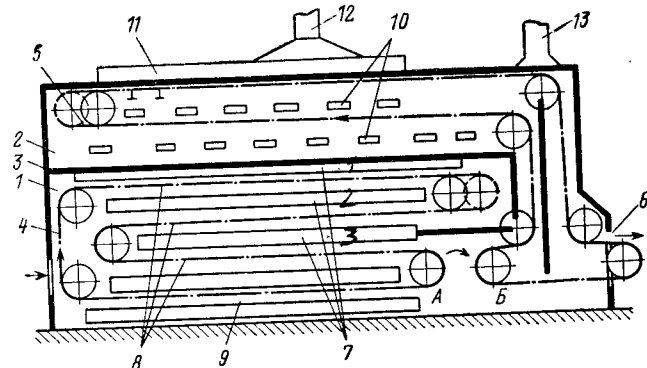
Схема сушилки ГИКИ для двухстадийной сушки тарелок
